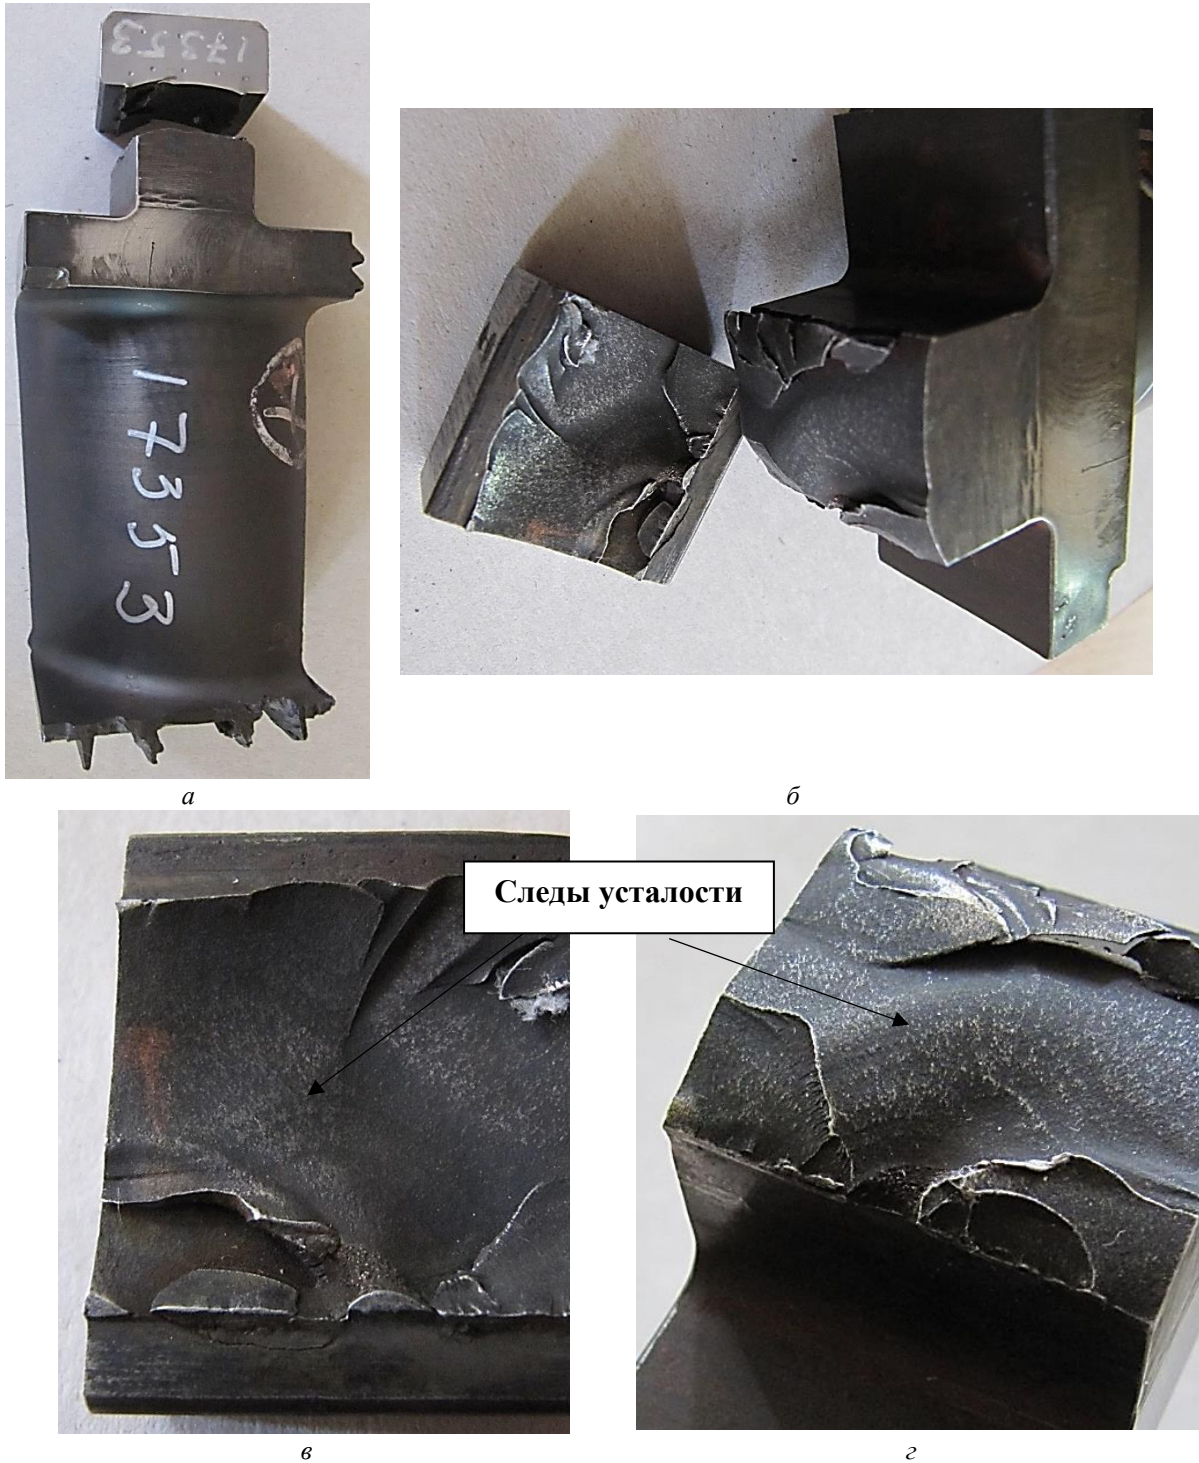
Разрушенная лопатка с маркировкой № 1: а – общий вид; б – излом и ответная часть излома хвостовика; в - з – следы усталости на поверхности излома
